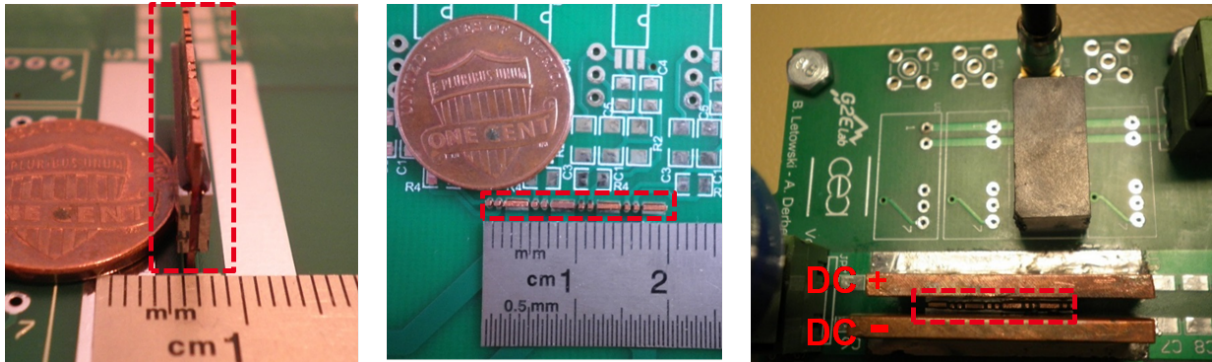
Photos du module 3D enfiché perpendiculairement dans le PCB
